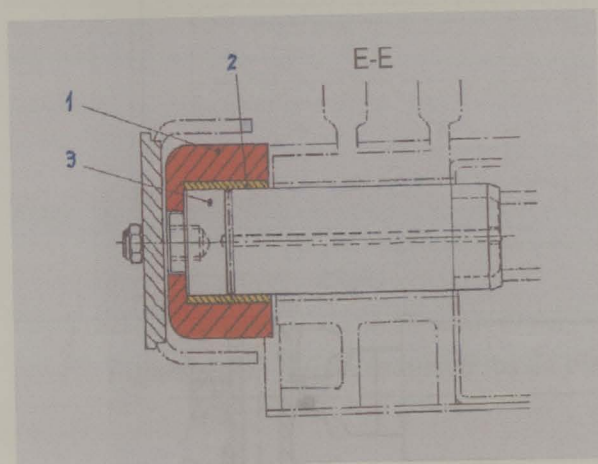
Corte do conjunto do charriot mostrando a montagem do rolete superior.
